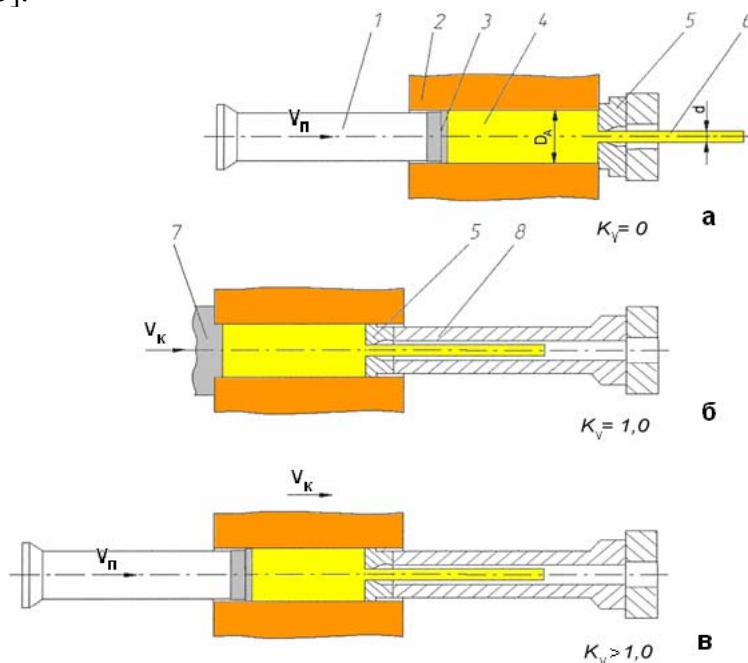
Схемы прессования: а) прямое; б) обратное; в) с активным действием сил трения: 1 – пресс-штемпель; 2 – контейнер; 3 – пресс-шайба; 4 – заготовка; 5 – матрица; 6 – изделие; 7 – пробка; 8 – полый пресс-штемпель
